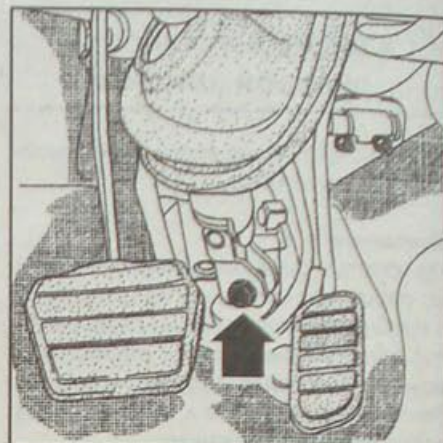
Расположение гайки и болта крепления карданного шарнира рулевого вала к рулевой передаче
